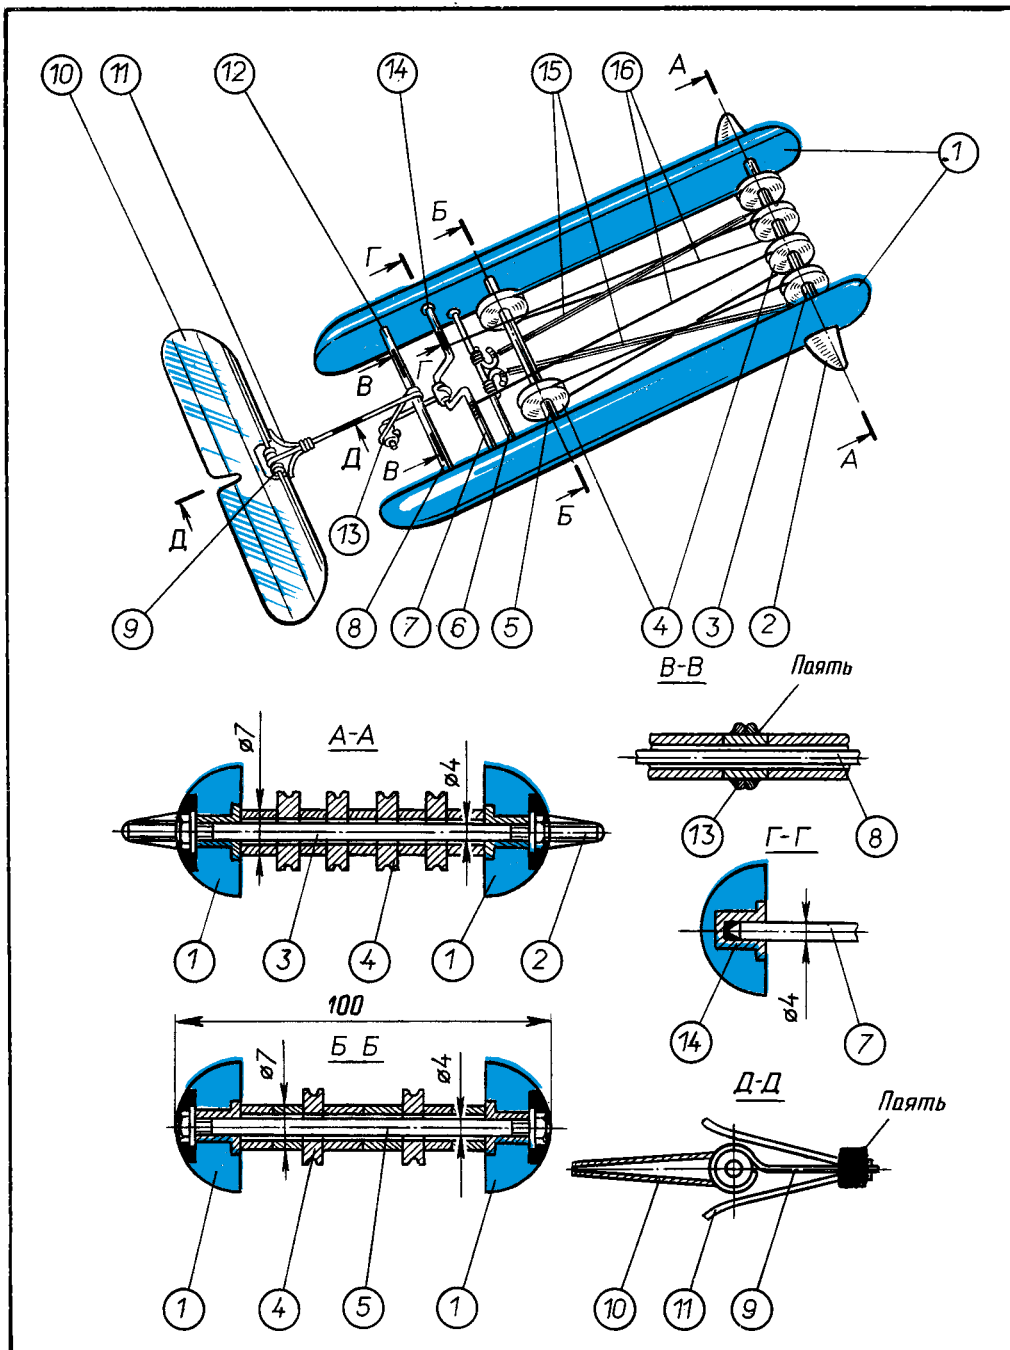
Модель катамарана с плавниковым двигателем: 1 — поплавки корпуса модели; 2 — рули; 3 — передняя ось с четырьмя роликами полиспата; 4; 5 — промежуточная ось с двумя роликами полиспата; 6 — коленчатый вал; 8 — задняя ось; 9 — плавниковый стебель; 10 — плавник; 11 — упоры; 12 — втулка; 13 — шатун; 14 — подшипники; 15 — резиновые жгуты; 16 — гибкие тяги
